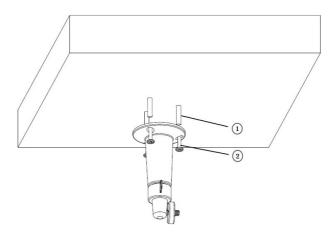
Fixação do suporte de montagem da Câmera
